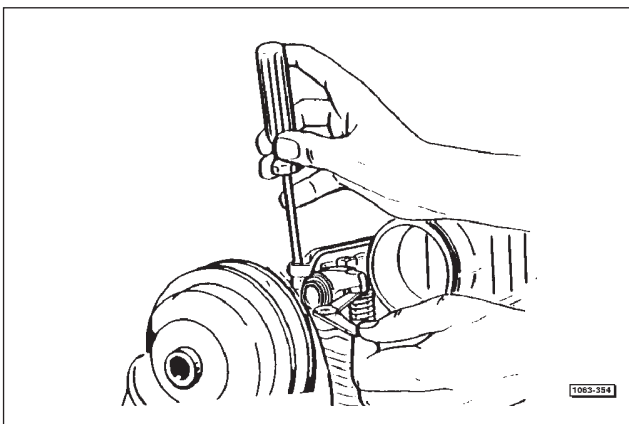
Régler le jeu entre soupapes et culbuteurs.
